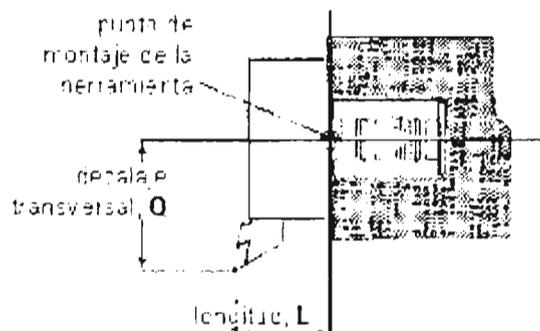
Dimensiones básicas de una herramienta de torno.
